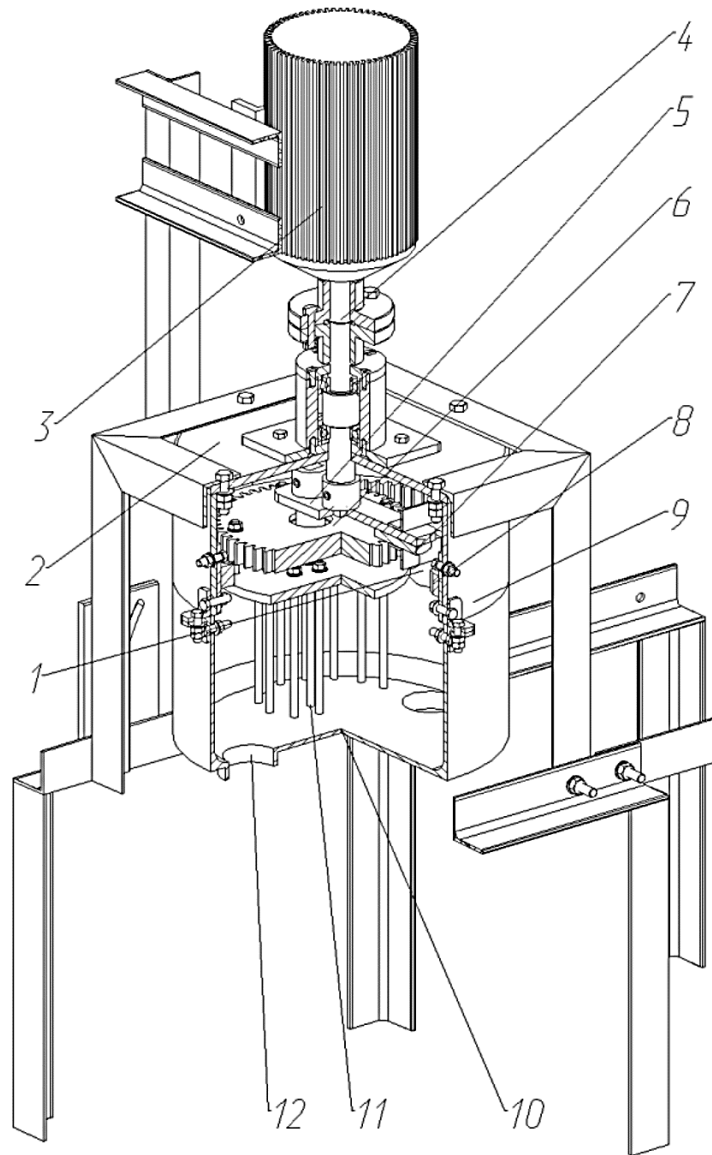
Конструкція планетарного змішувача: 1 - завантажувальний пристрій; 2 – кришка корпусу; 3-двигун; 4 – вихідний вал; 5 – повідець; 6 - шестерня; 7 - противага; 8 – зубчастий вінець; 9 – корпус; 10 – ємність; 11 - мішалка; 12 – розвантажувальний пристрій
